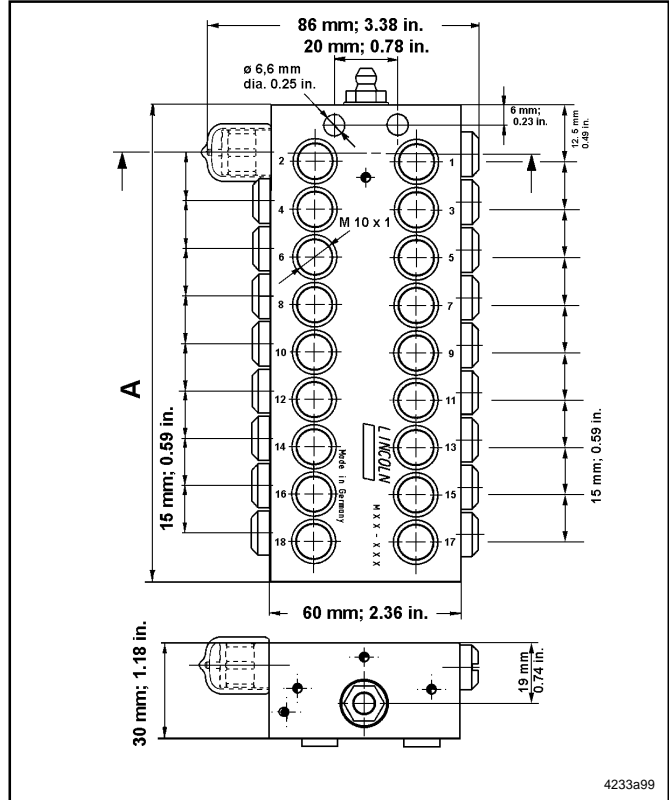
Cotes dimensionnelles du doseur SSV installé en arrière
